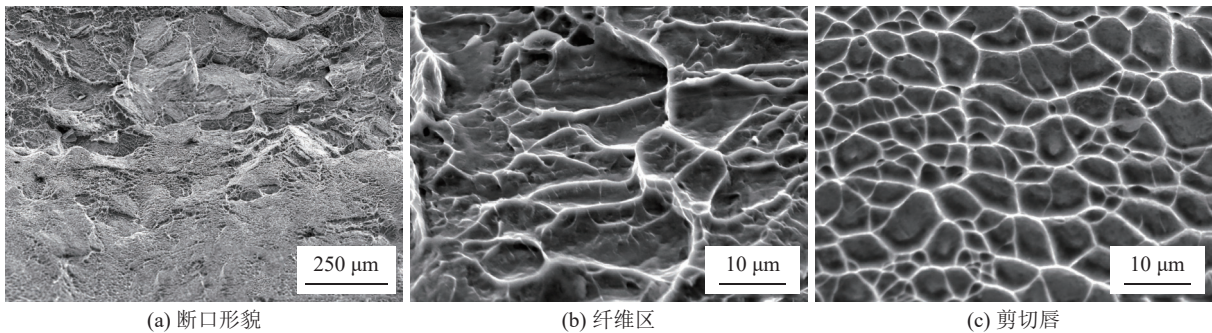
TC4 钛合金电子束焊接头 1 拉伸断口形貌
